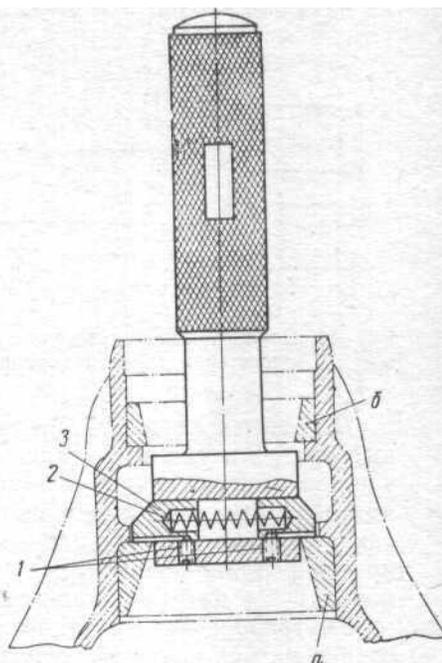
Оправка для выпрессовывания наружного кольца заднего подшипника вала ведущей шестерни главной передачи:
